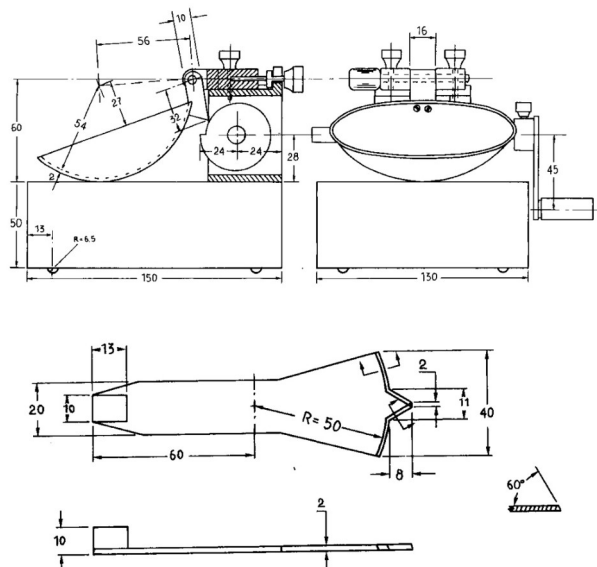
Dimensioni standard del cucchiaio e del solcatore.
